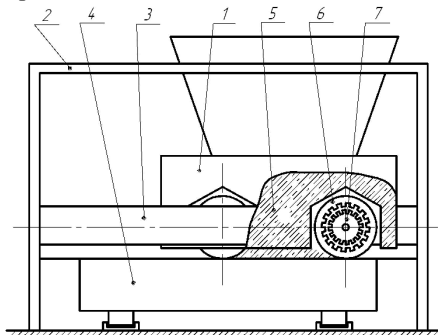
Роликовая формовочная установка с приводом от шагового двигателя
